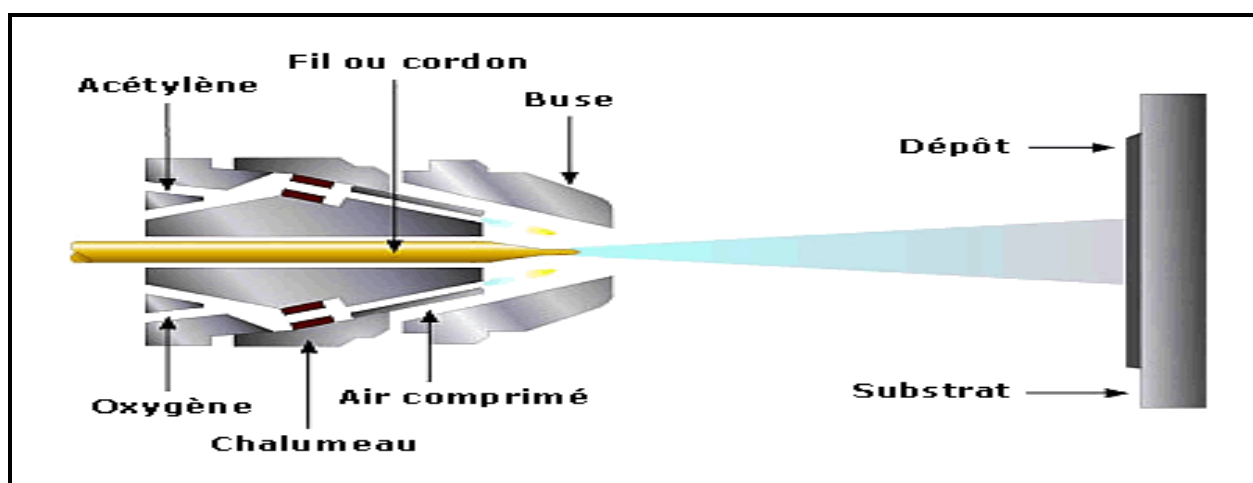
schéma de principe de la projection thermique à Flamme-fil [29].
